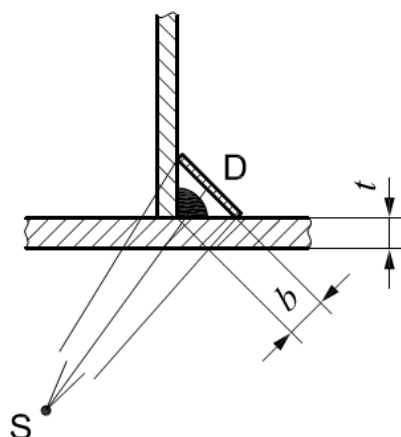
Схема контроля при просвечивании угловых сварных швов
